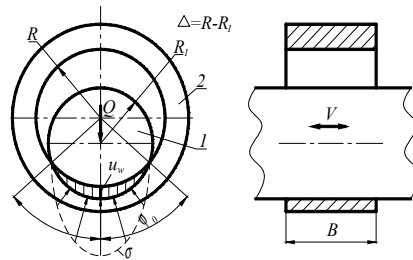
Розрахункова схема циліндричної напрямної ковзання
